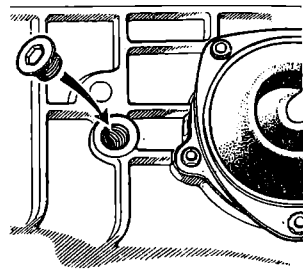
Пробка для заливки и контроля масла в коробке передач.
